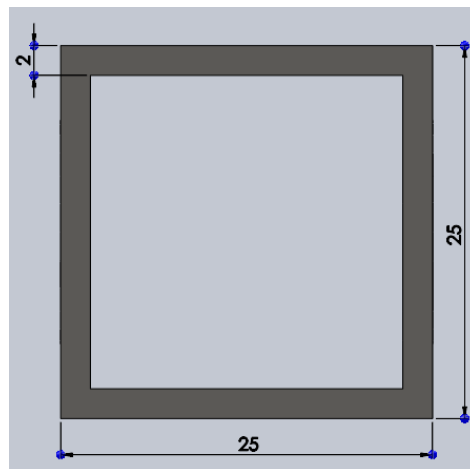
VIGA PARA SISTEMA DE ARRASTRE
